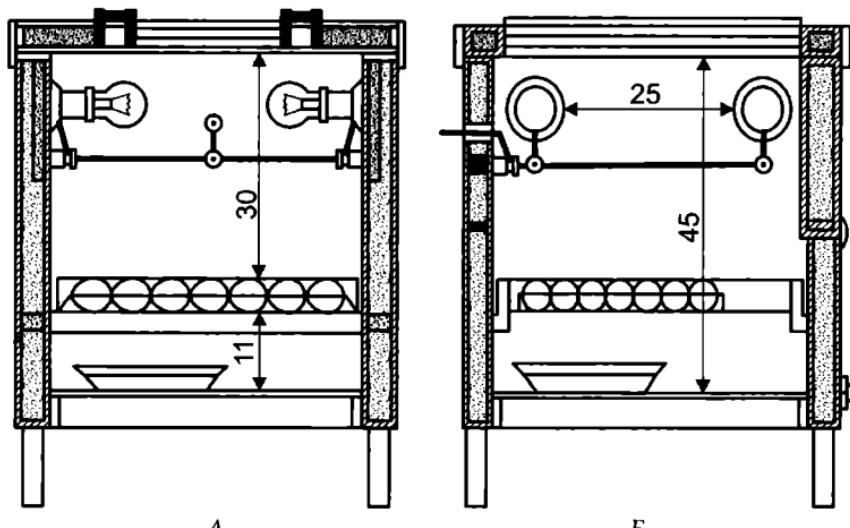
Инкубатор конструкции Н. П. Третьякова в разрезе:
